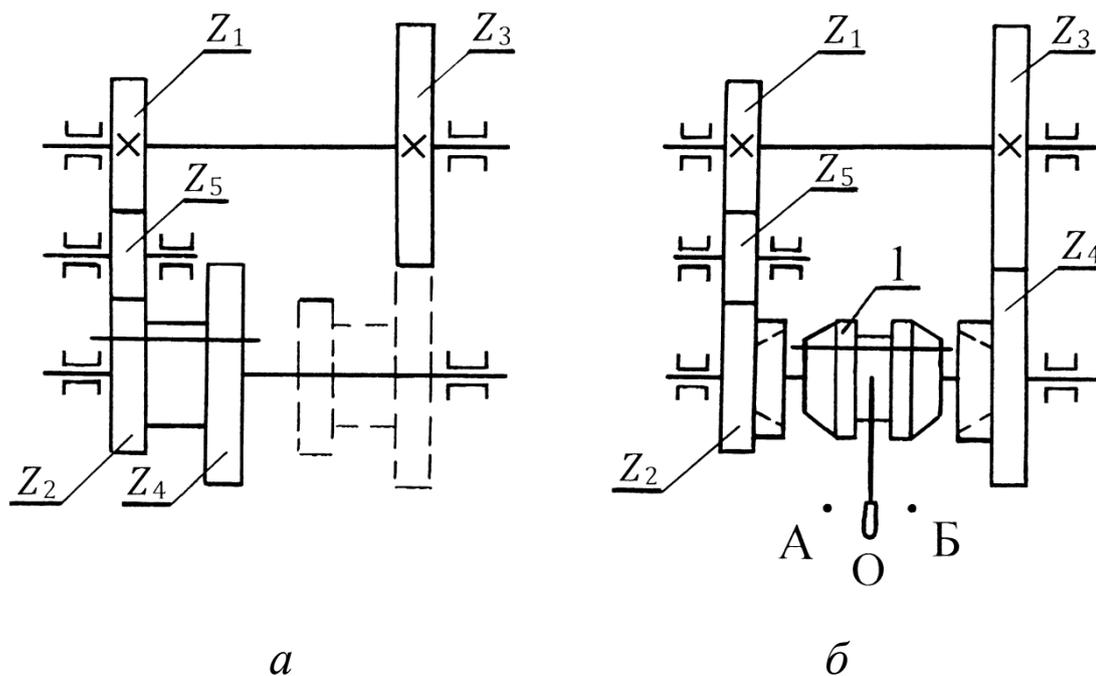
Реверсивные механизмы с цилиндрическими зубчатыми колёсами:
